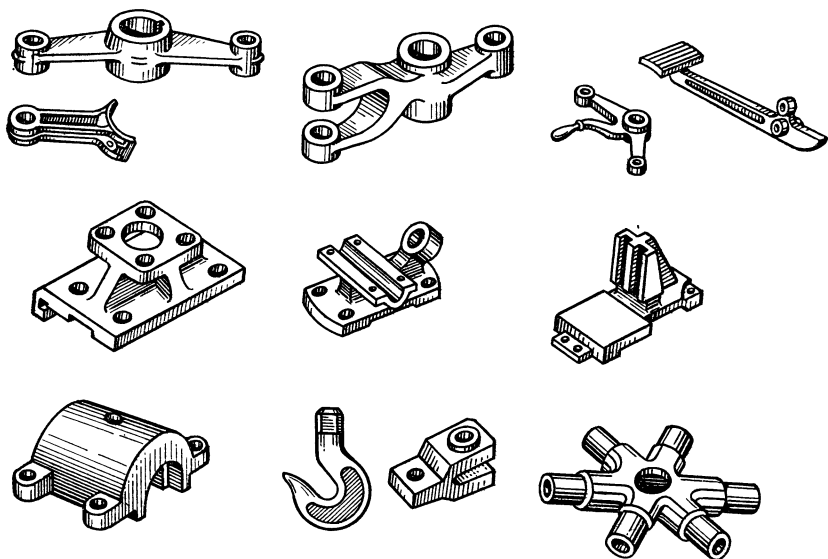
Укрупненный классификатор деталей типа рычагов, шатунов, кронштейнов фасонных крышек и др.
